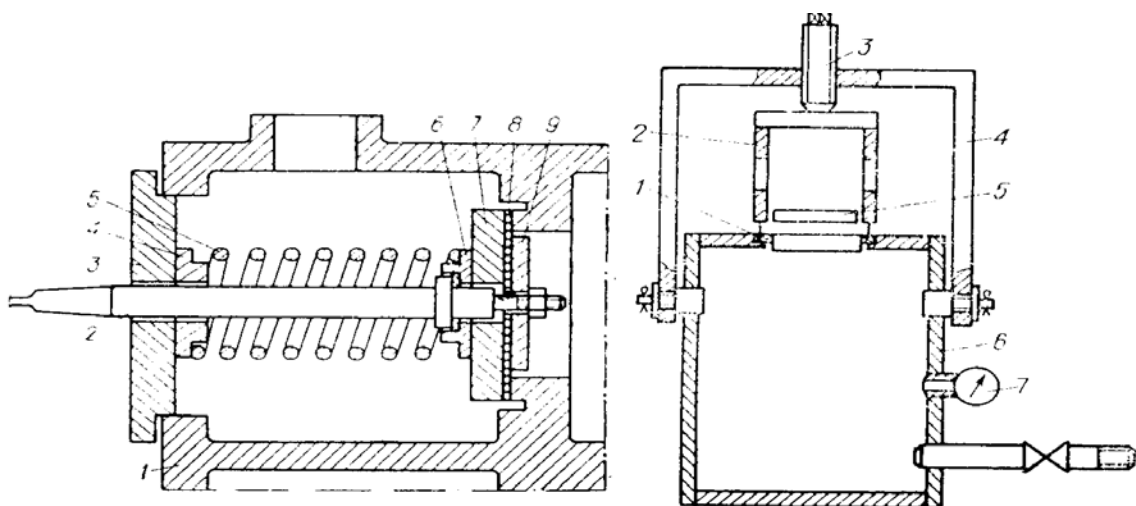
Приспособление для притирки посадочной поверхности цилиндра под клапан:
